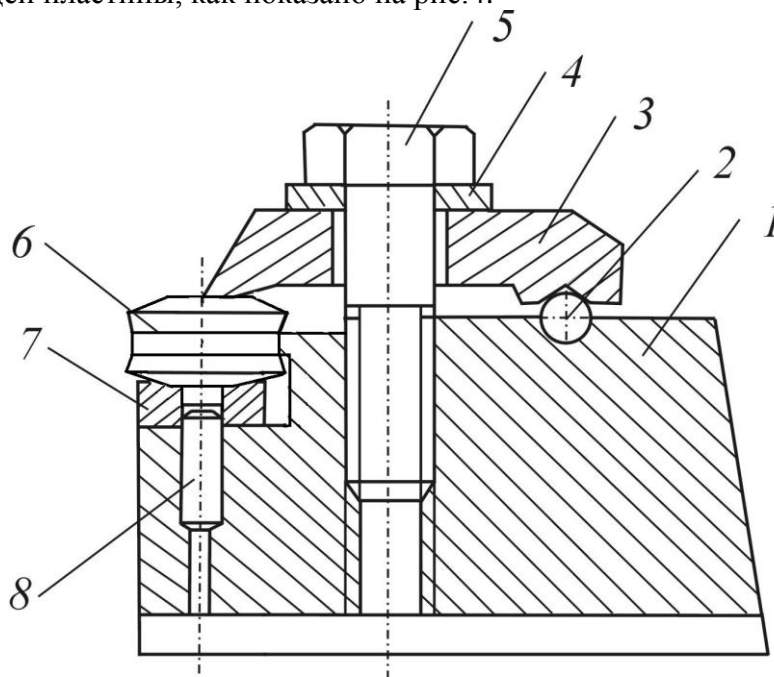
Конструкция резцовой державки: 1—корпус, 2—опорный шарик, 3—прижим, 4—шайба, 5—винт, 6—режущая пластина, 7—сепаратор, 8—штифт
